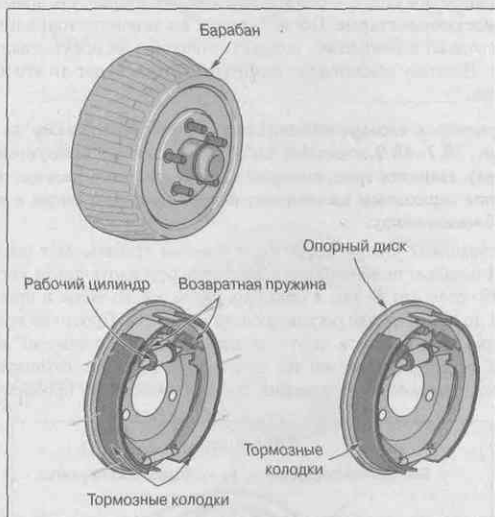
Конструкция тормозного механизма барабанного типа
